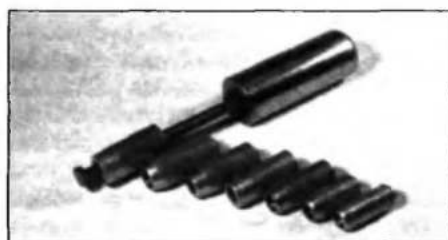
Оправка с набором пилотов для сборки шатунов с поршнями (при неподвижной посадке пальца в шатуне)
